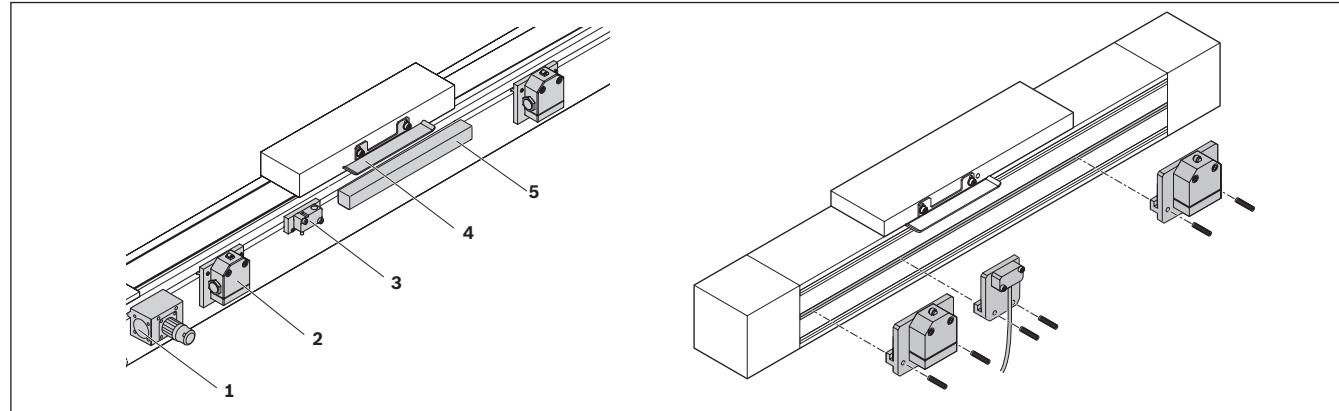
Übersicht mechanische Schalter, induktive Sensoren, Dose-Stecker, Kabelkanal, Schaltwinkel
